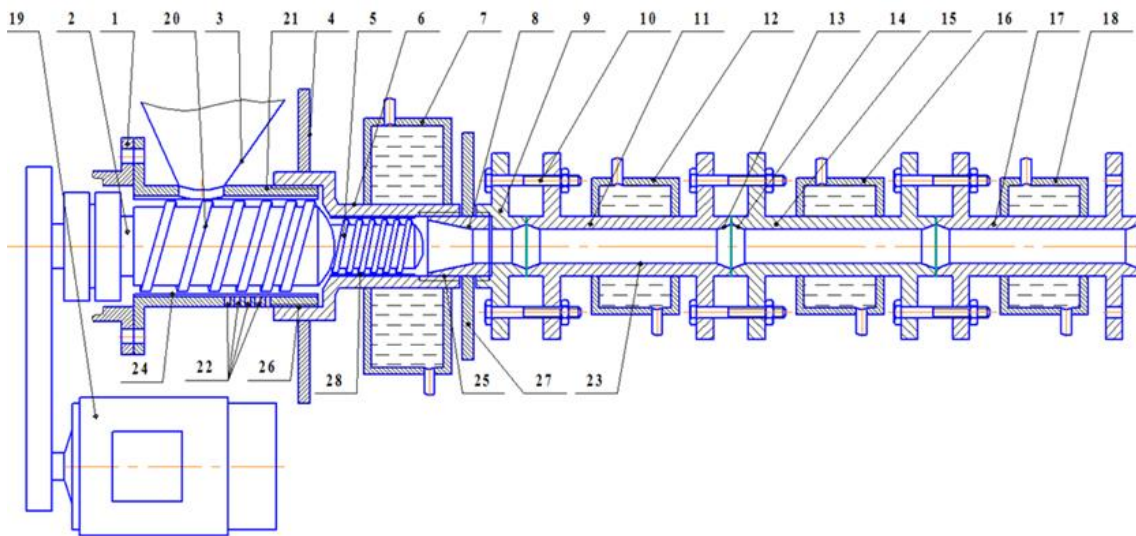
Схема шнекового прес-екструдера для отримання паливних брикетів з пристроєм остаточного формування: 1 – підшипниковий вузол; 2 – вал приводу; 3 – бункер; 4 – фіксатор; 5, 20 – шнек; 6 – камера дожиму; 7, 12, 16, 18 – сорочка охолодження; 8 – матриця; 9 – пристрій остаточного формування; 10 – болт; 11, 15, 17 – секції труб; 13, 14 – масло згінні фаски; 19 – електродвигун; 21 – пресуюча камера; 22 – отвори для відводу масла; 23 – труба; 24, 28 внутрішні ребра; 25, 26 – різьбове з'єднання; 27 – рукоятка.
